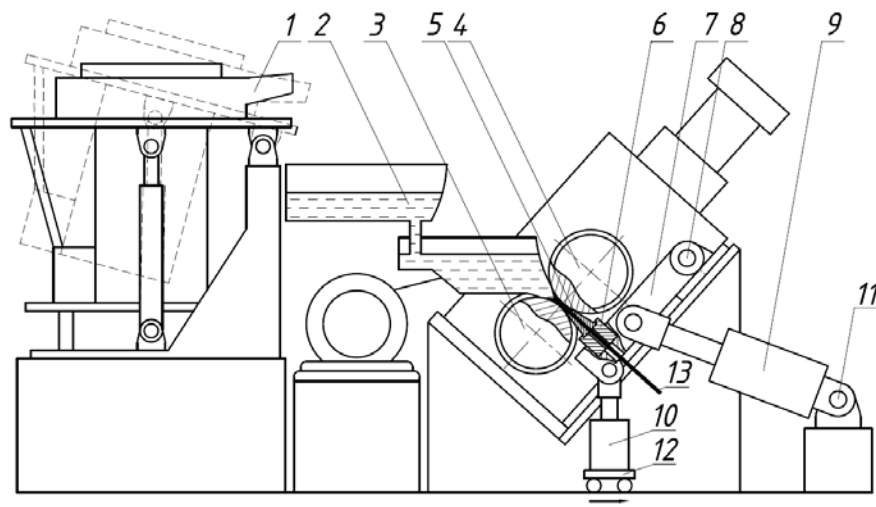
Общий вид устройства по патенту РФ №128529: 1 - печь-миксер; 2 - литниковая система; 3 - валок с ручьем; 4 - валок с выступом; 5 - матрица; 6 - матрицедержатель; 7 - кронштейн; 8, 11, 12 - шарниры; 9 - гидроцилиндр; 10 - вертикальный гидроцилиндр
